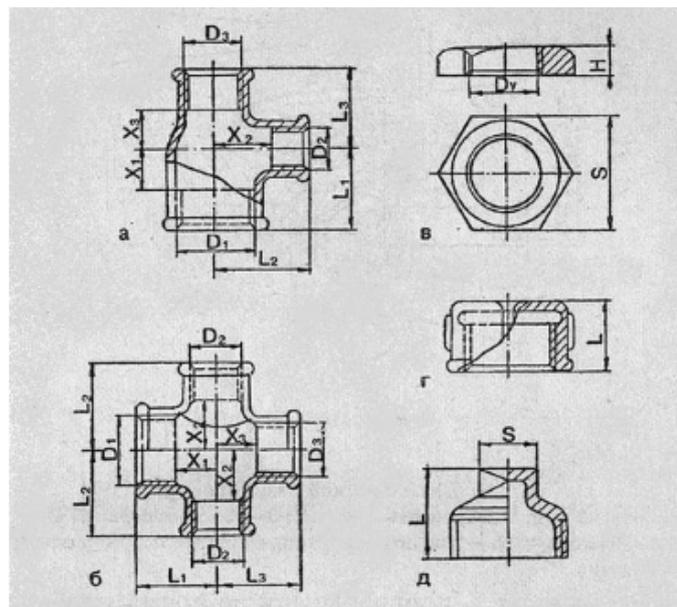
Соединительные части из ковкого чугуна: а — тройник с двумя переходами; б — крест с двумя переходами; в — контргайка; г — колпак; д — пробка
